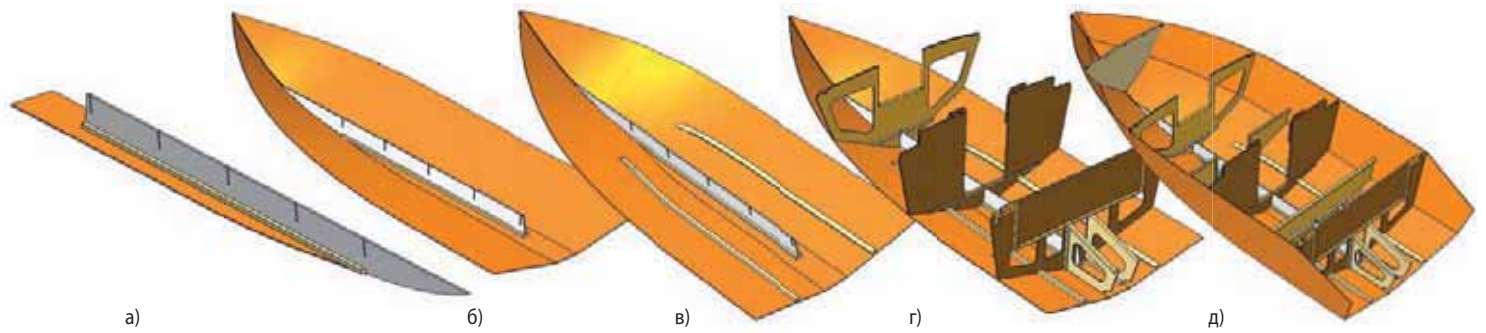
Стадии сборки корпуса и конструкция узлов стыка деталей
